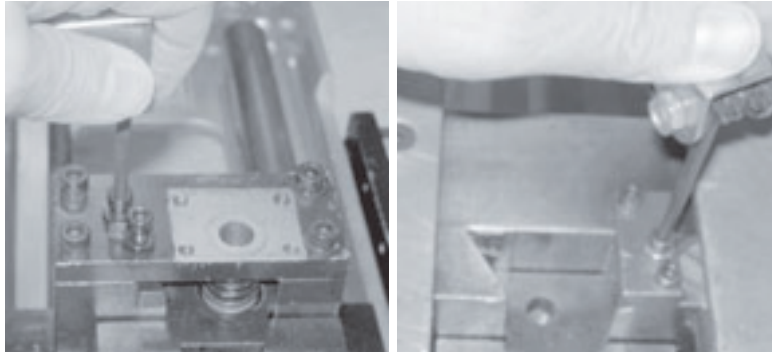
Para ajustar la tensión del portaherramientas, retraiga los tornillos de ajuste frontal (izquierda), luego atornille el tornillo de ajuste posterior.
